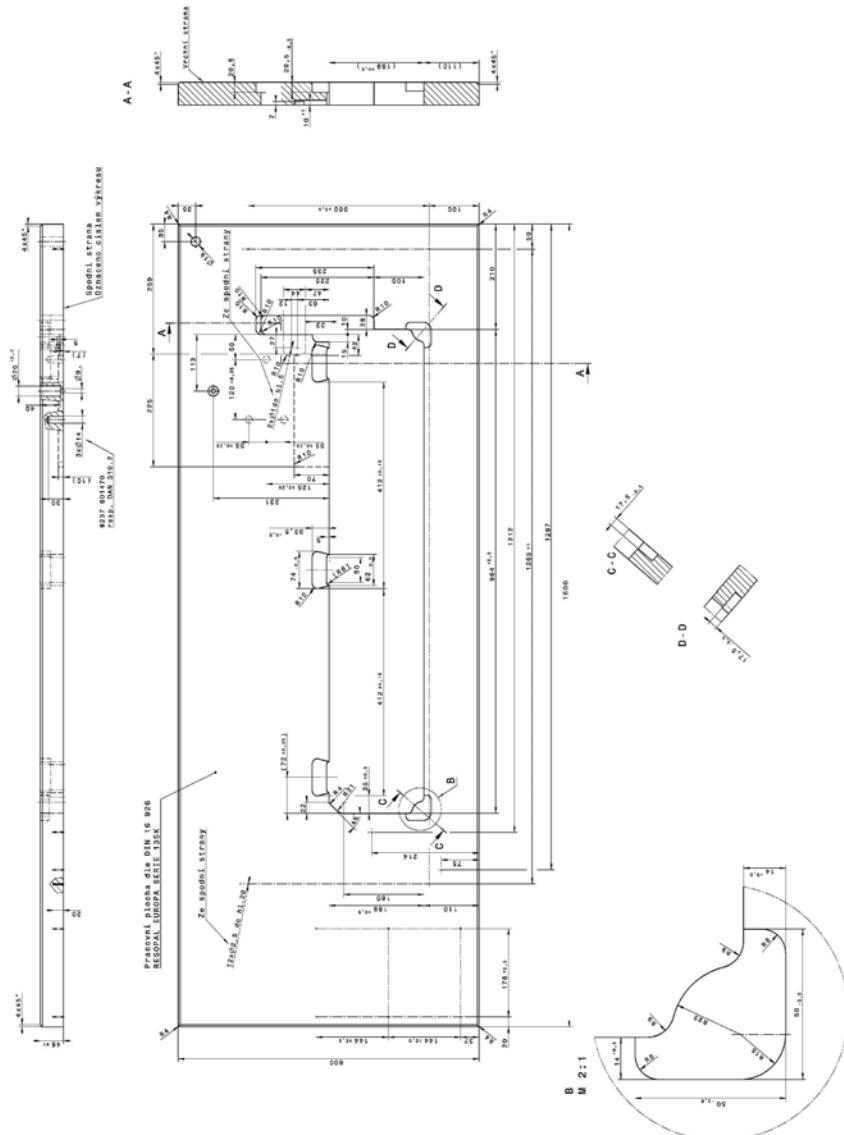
Umístění komponent na spodní stranu desky podstavce 2
